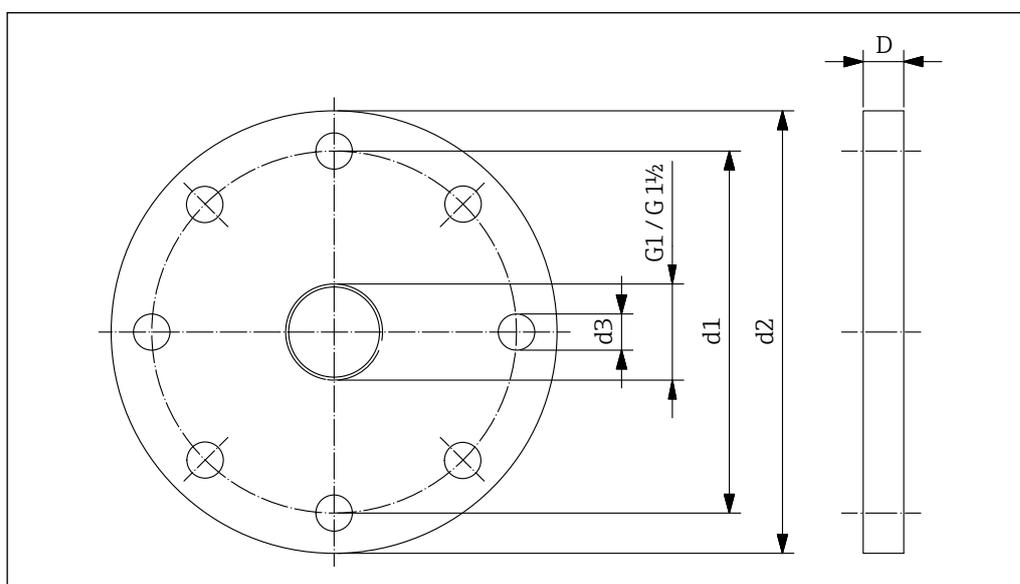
Dimensiones adaptador para soldar FAR52. Unidad de medida mm (in)
